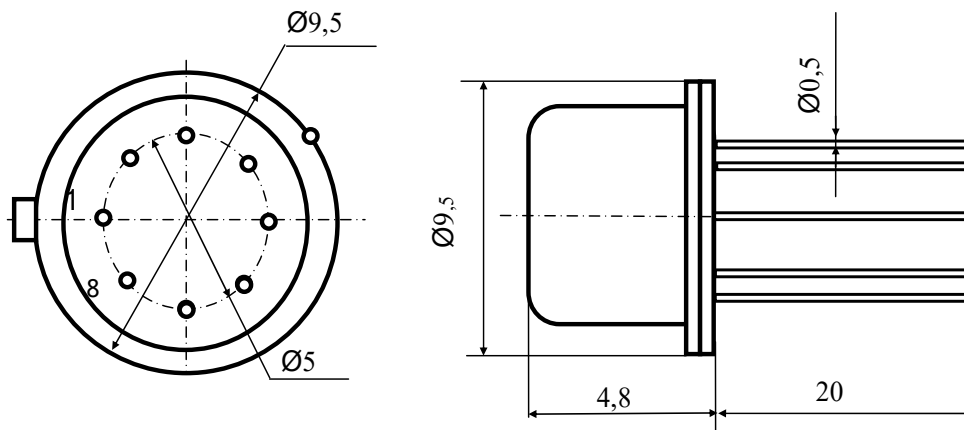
Внешний вид и габаритные размеры аналоговой микросхемы в корпусе 301.8-2
